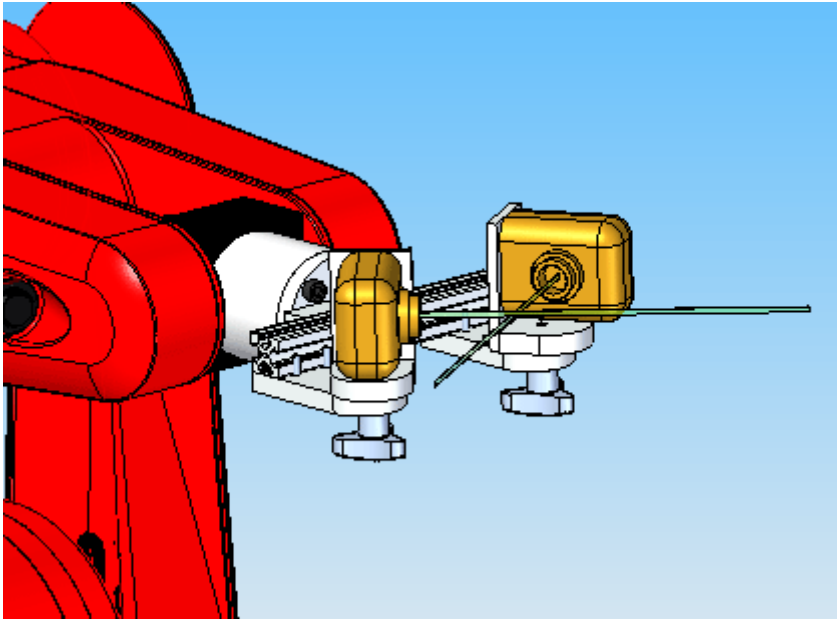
Conjunto formado por dos cámaras en la brida del robot.
